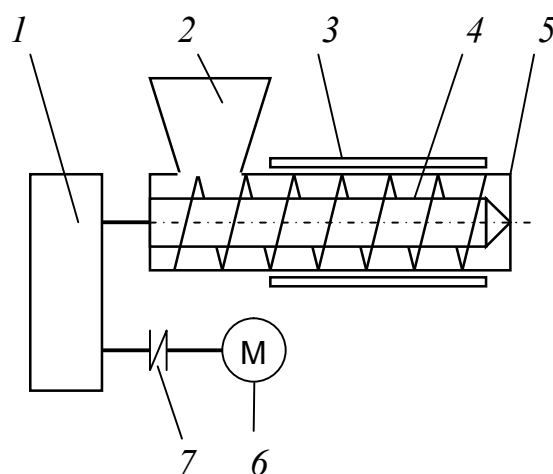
Схема одночерв'ячного екструдера: 1 – редуктор; 2 – завантажувальний отвір; 3 – електронагрівник; 4 – черв'як; 5 – корпус; 6 – електродвигун; 7 – муфта
